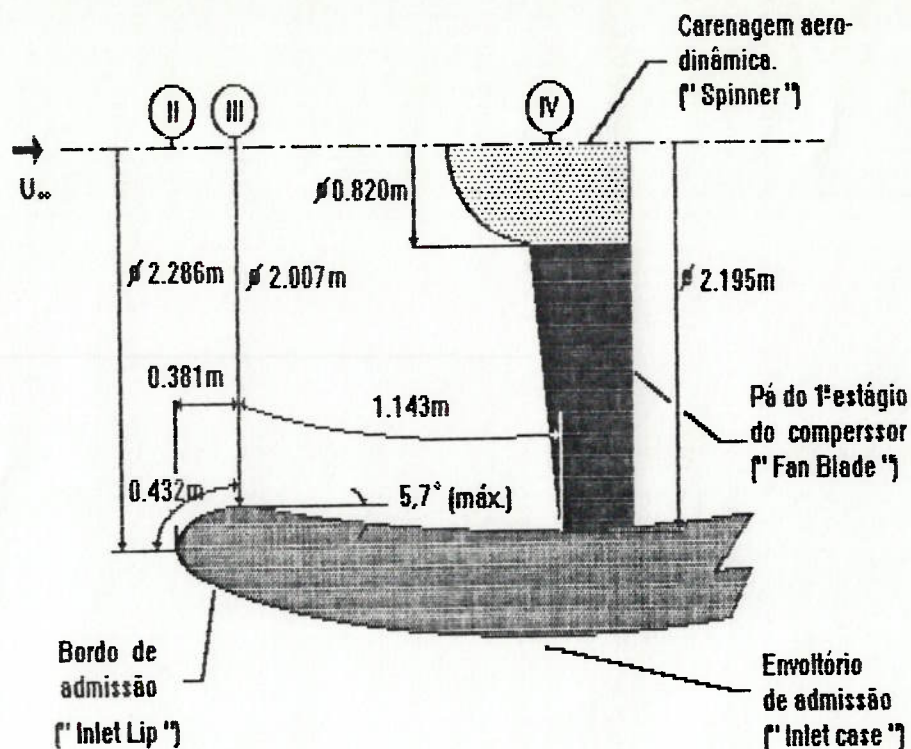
Geometria do bocal de admissão do motor CF6-80A, conforme instalado em aeronave Boeing 767-200. ( Dimensões obtidas por medição direta. Esquema sem escala ).
